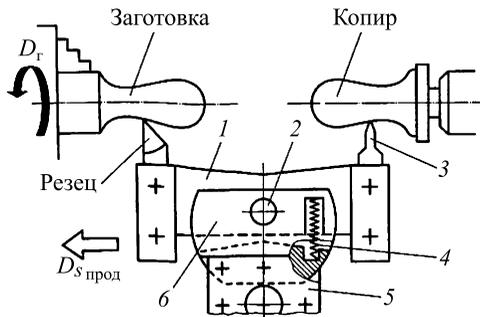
Приспособление для обработки фасонной поверхности:
